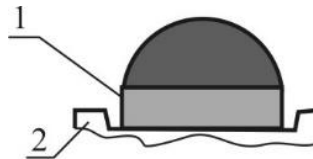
Вигляд відновленої напайки циліндричним інструментом
